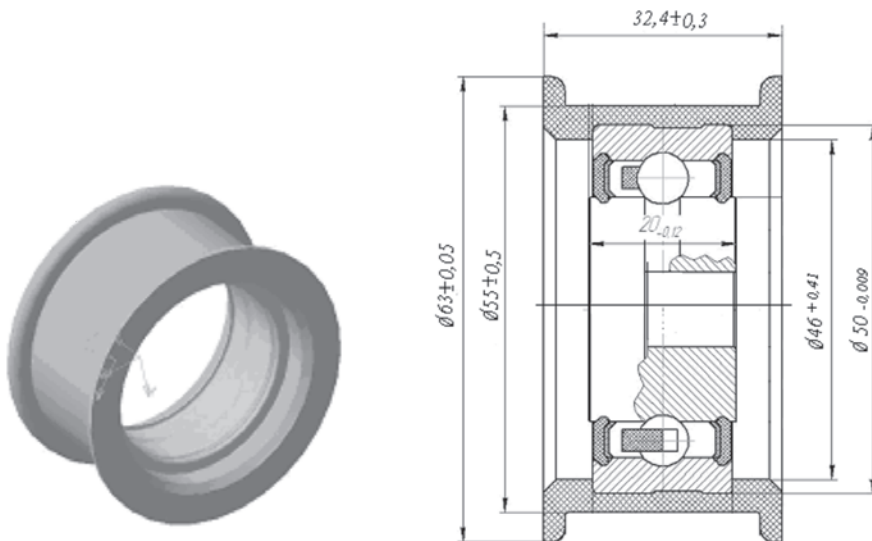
Наружное кольцо подшипника 2108-1006120-01 с ребордами из полиамида
